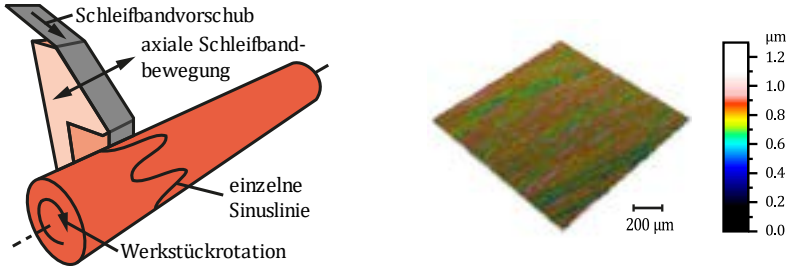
Superfinishen nach [103, 104] Bild 2.16: Supergefinishte Oberfläche
